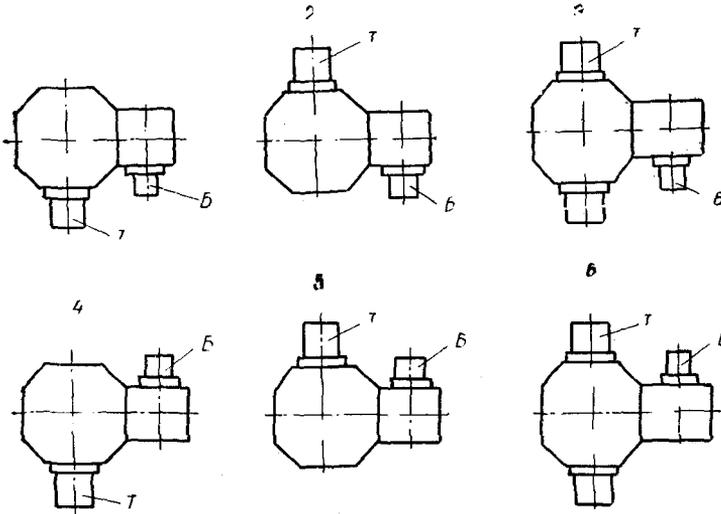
Схемы сборок (1—6) редуктора ЧДПМ 100/180:
